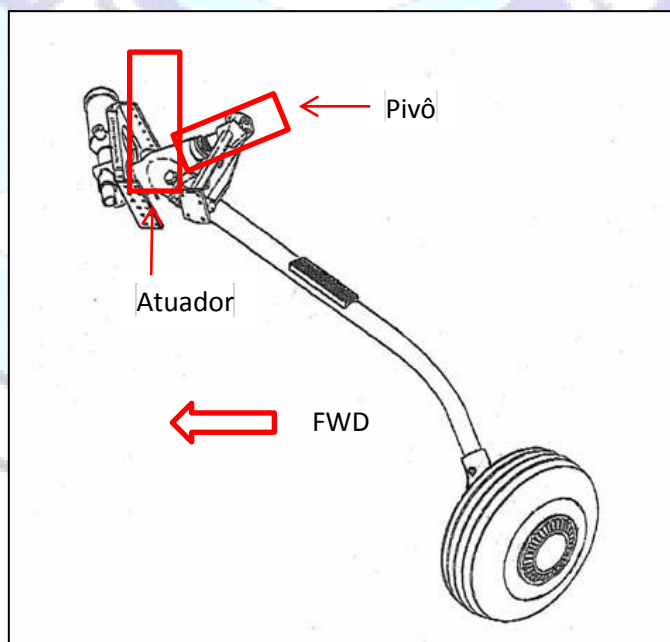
Conjunto da perna esquerda do trem de pouso principal.
